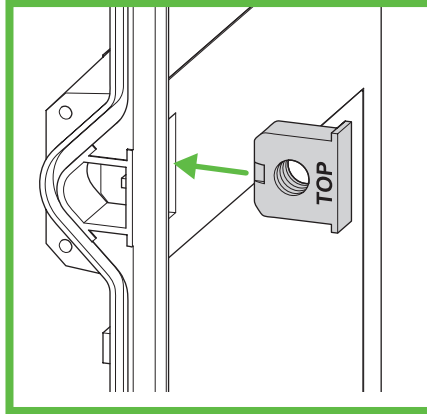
Montage Gewindeeinschübe GEOS 4050
